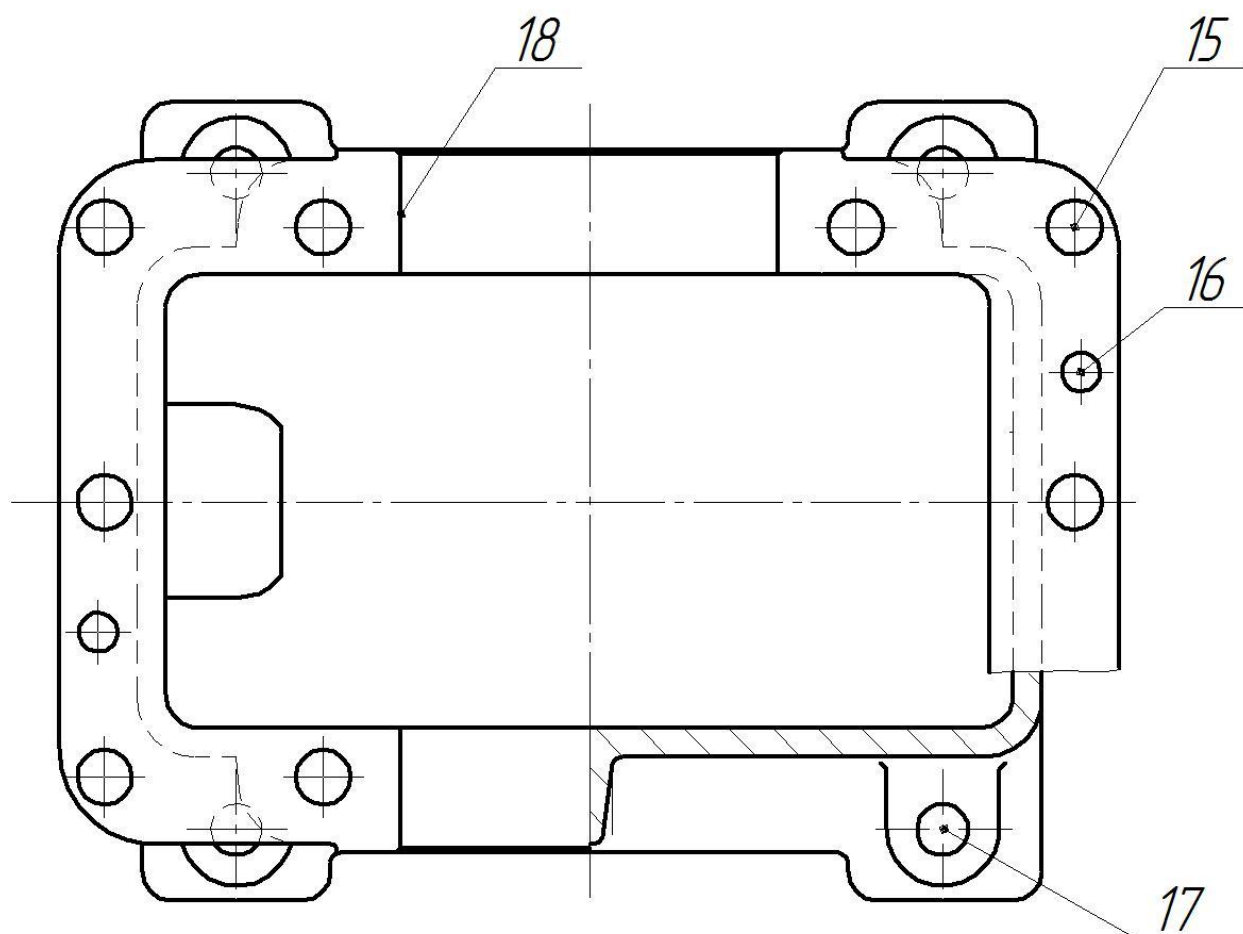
Вид сверху корпуса червячного редуктора
